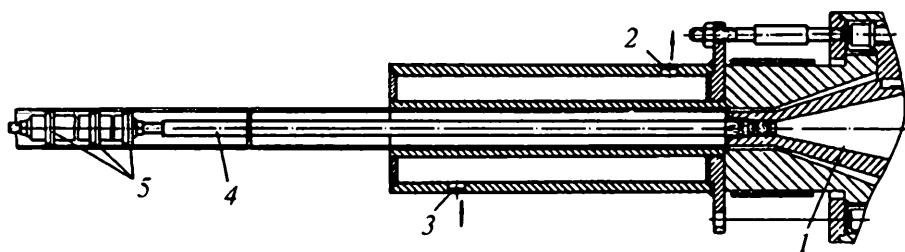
Калибрующая насадка для экструдруемых труб
